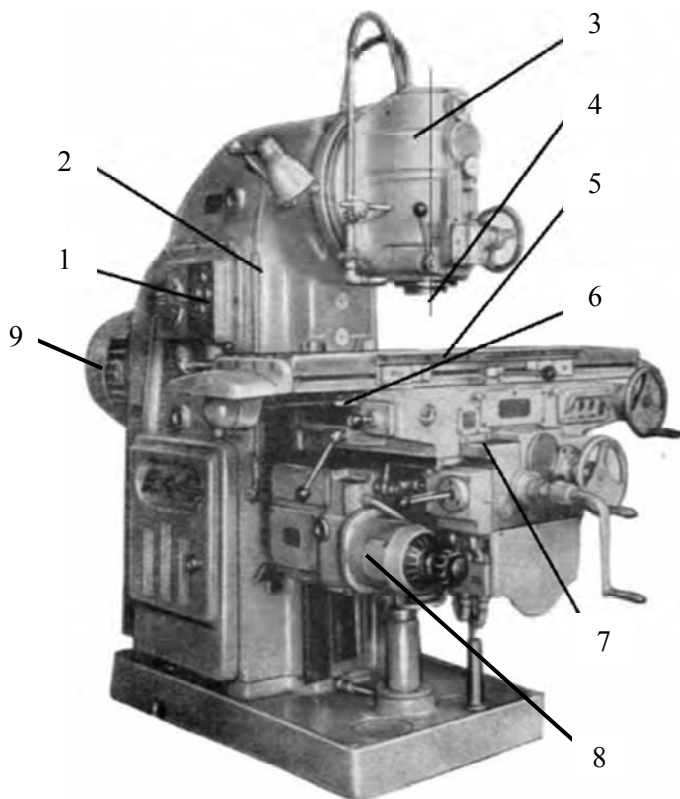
Общий вид вертикально-фрезерного станка модели 6M12П
